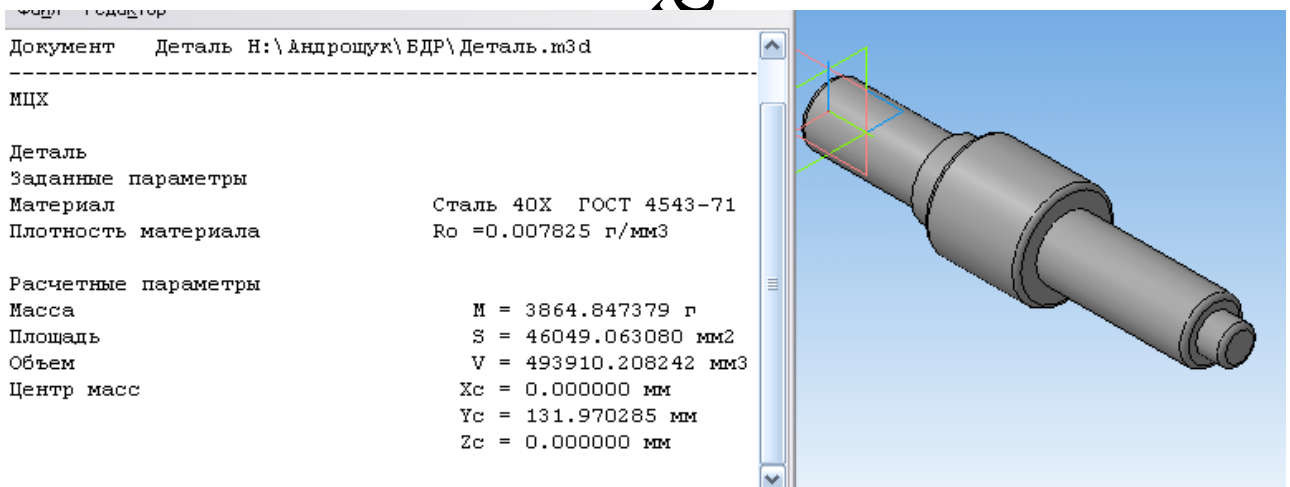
Визначення маси заготовки штампованої на КГШП
